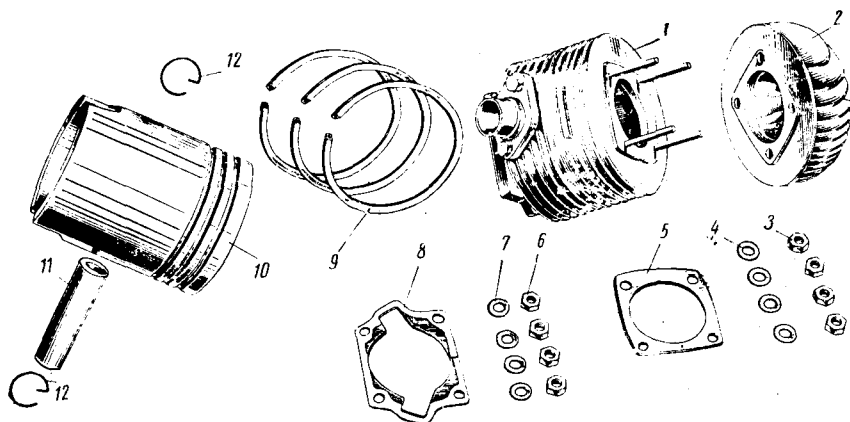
Цилиндро-поршневая группа двигателя мотороллера Т-200М:
